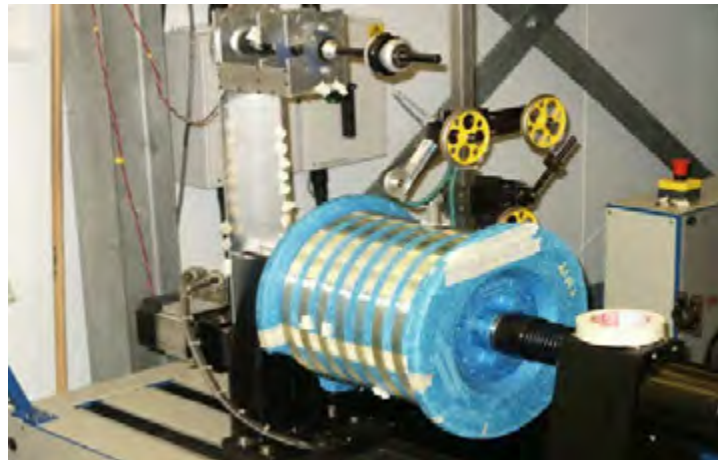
Mecanismo que enrolla la fibra en el tambor
